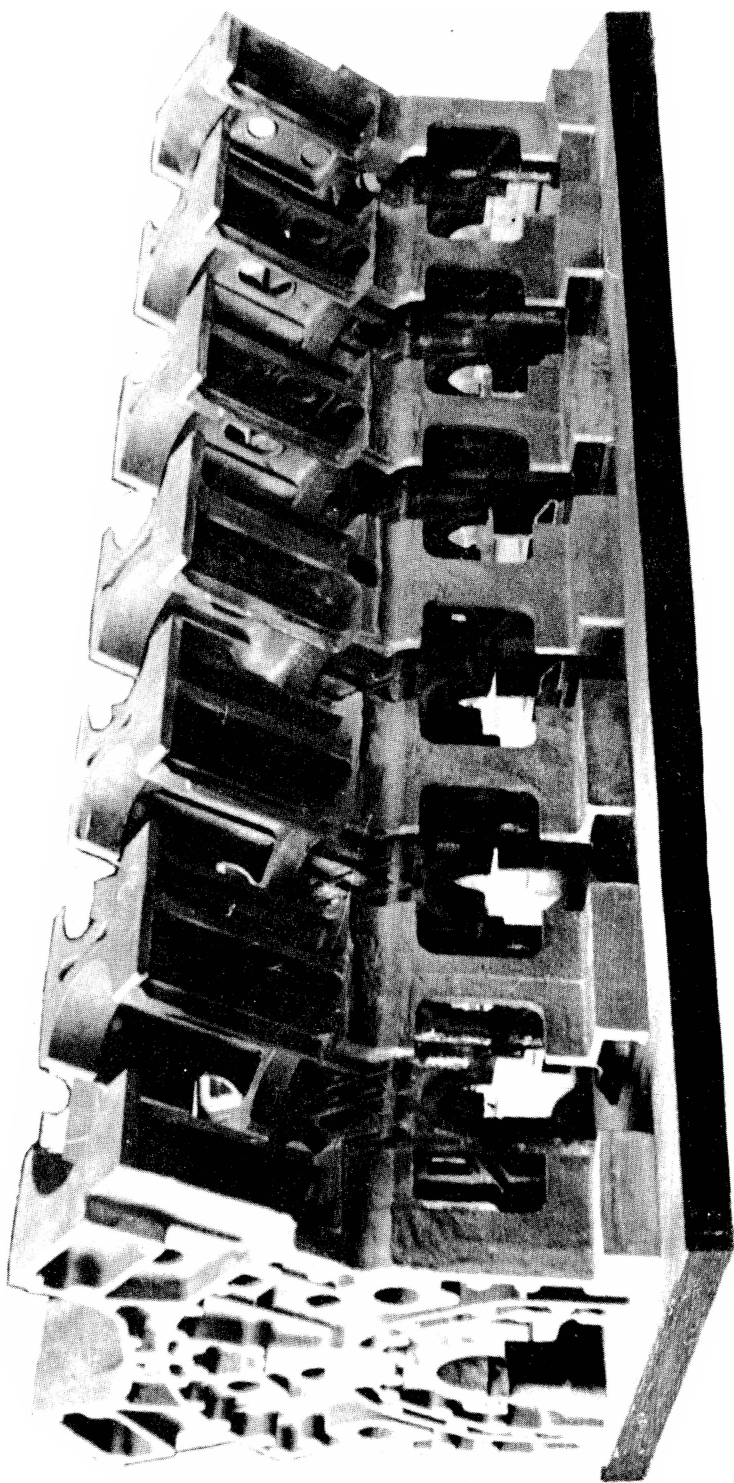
Bâti-cylindres en acier moulé. Eléments assemblés par soudure.
